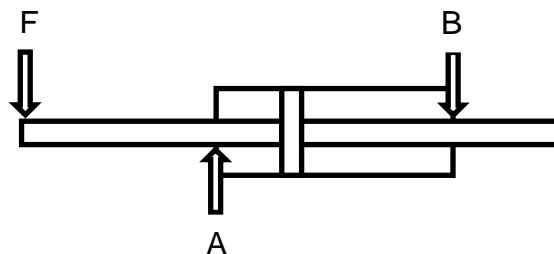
Gleichlaufzylinder, Vorzugsvariante
